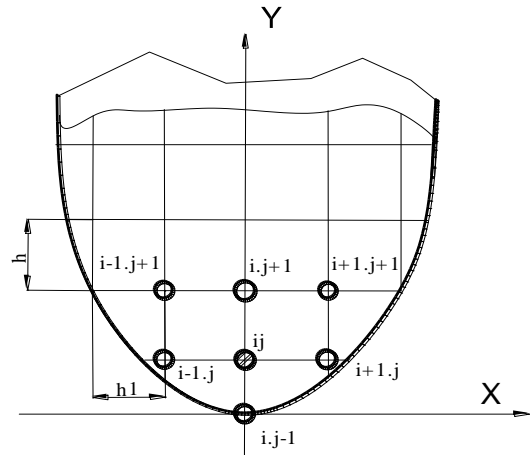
Схема сітки фіксованих комірок перетину ділянки заготовки в області обтікання колодки матеріалом заготовки
